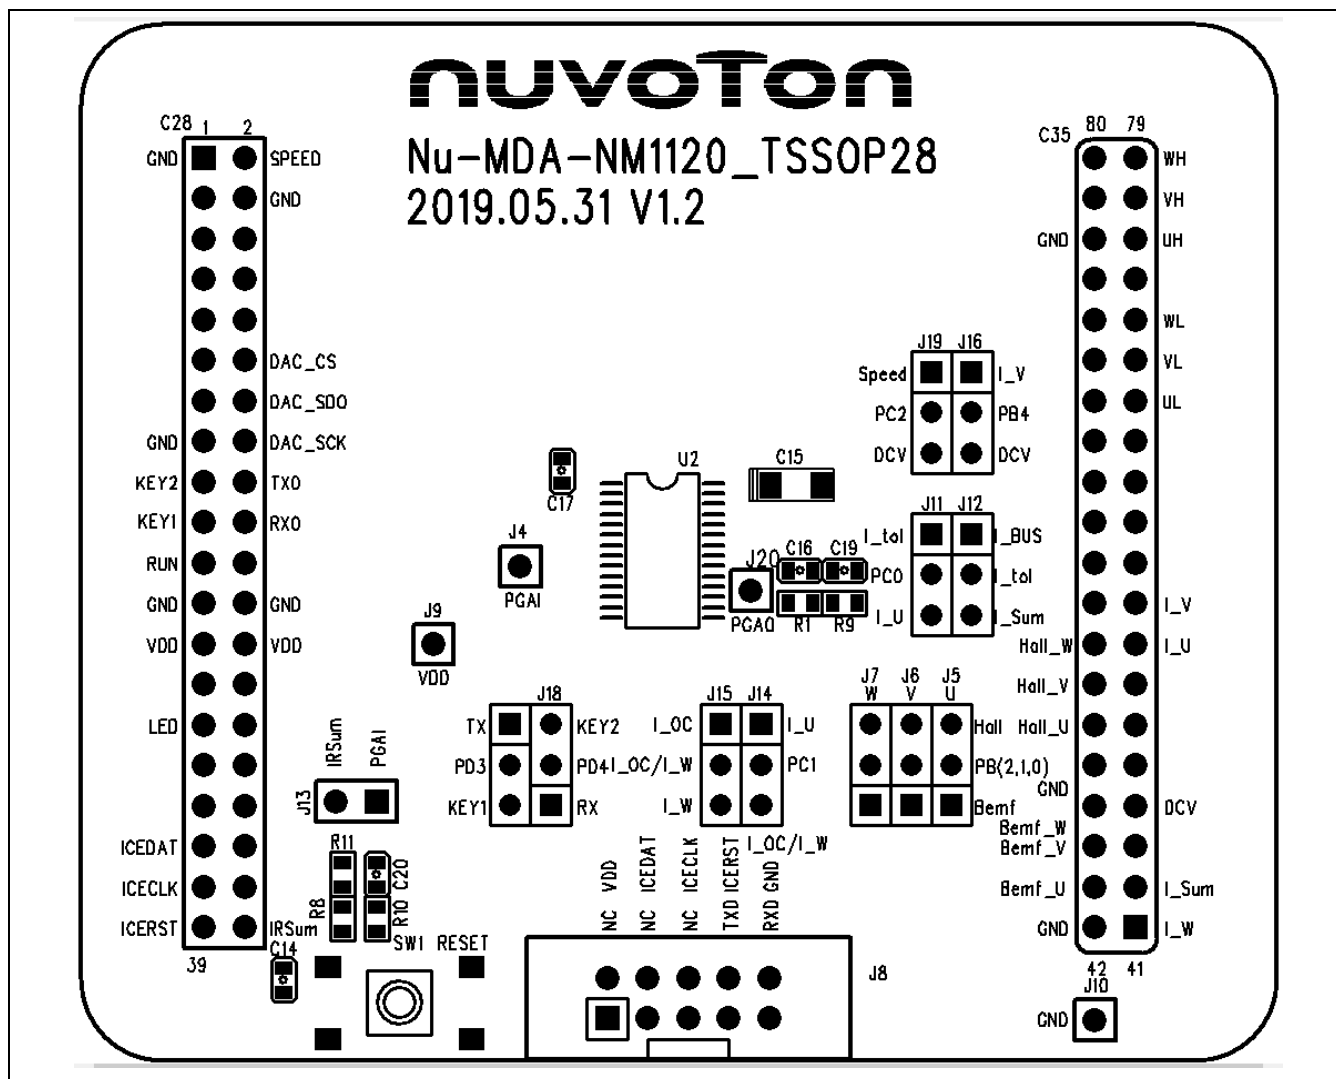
Nu-MDA-NM1120 PCB 佈局
